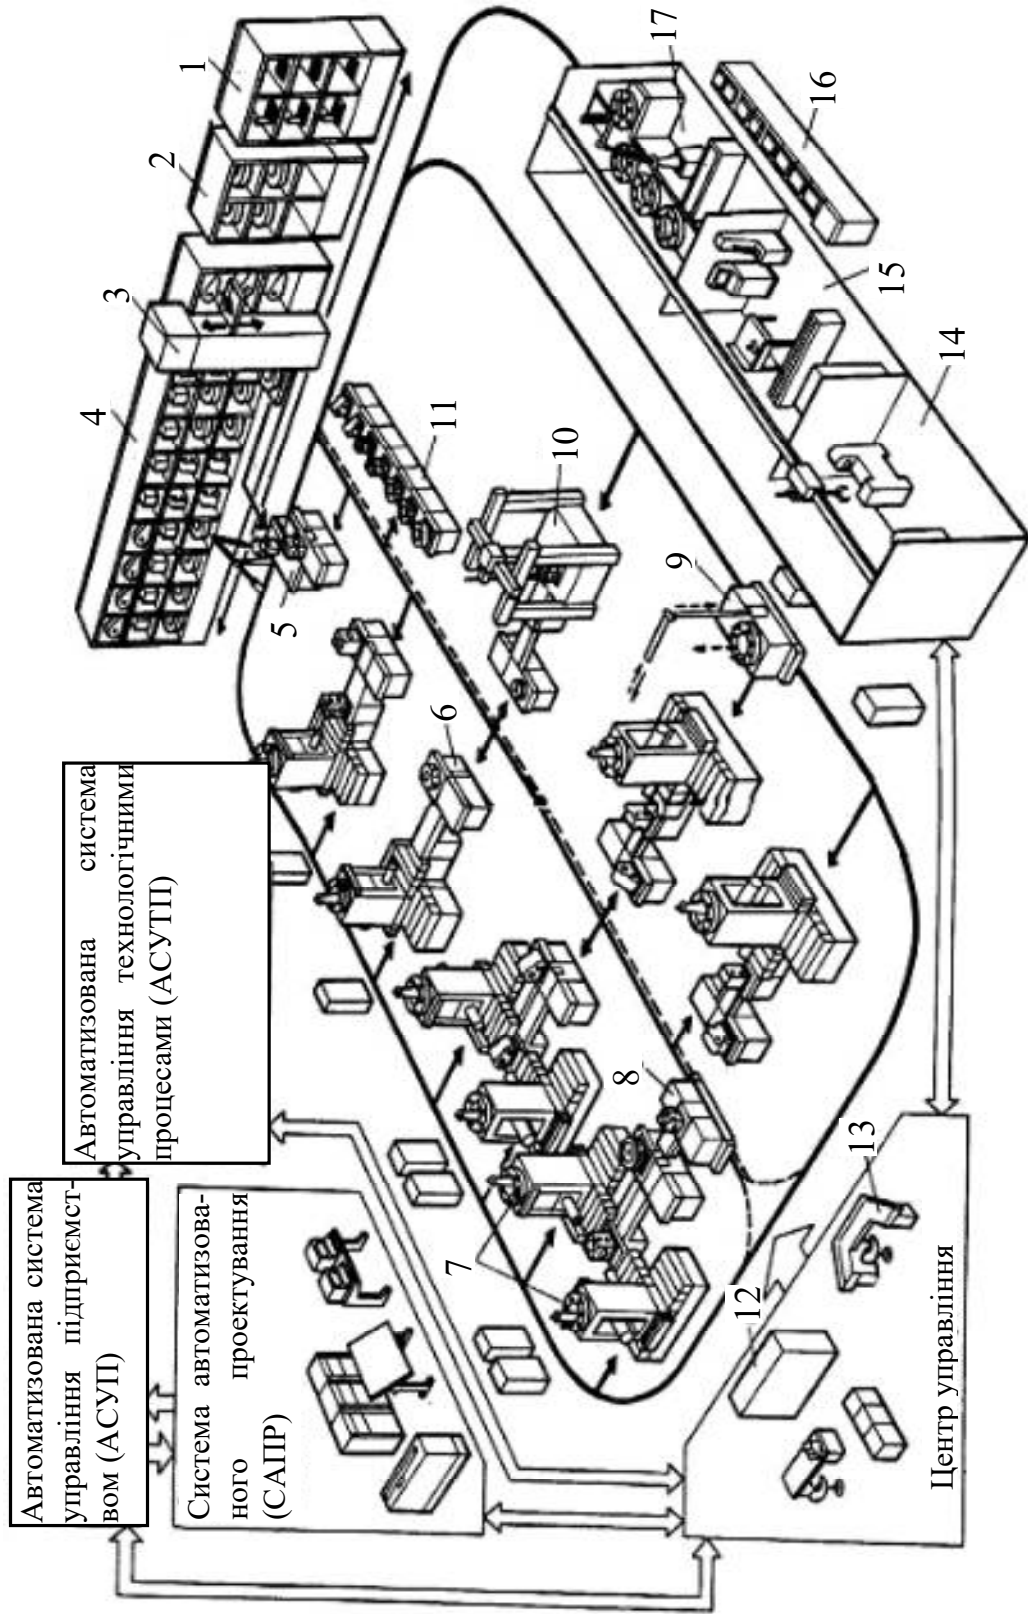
ГВС: 1 – склад палет; 2 – інструментальні магазини; 3 – штабелер, 4 – заготовки і деталі; 5 – монтажний стіл; 6 – накопичувач; 7 – верстати, 8, 9 – транспортні роботи; 10 – вимірювальна машина; 11 – накопичувач палет; 12 – БОМ; 13 – пульт оператора; 14 – ділянка заточування інструмента; 15 – ділянка комплектування та налаштування інструмента; 16 – ділянка складання палет; 17 – ділянка складання магазинів
